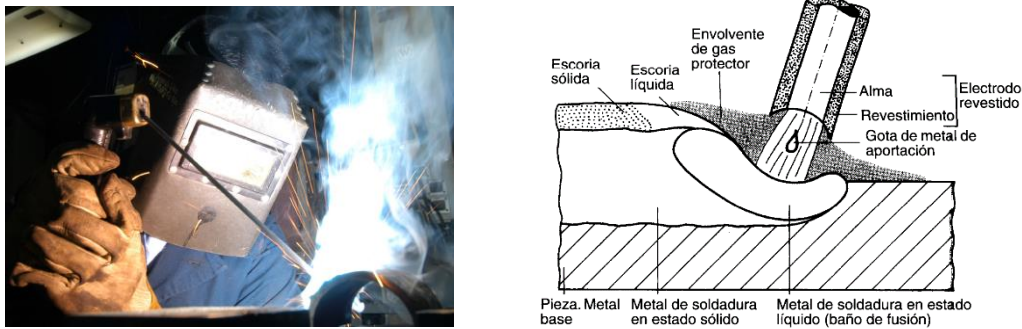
Soldadura SMAW (electrodo revestido)
